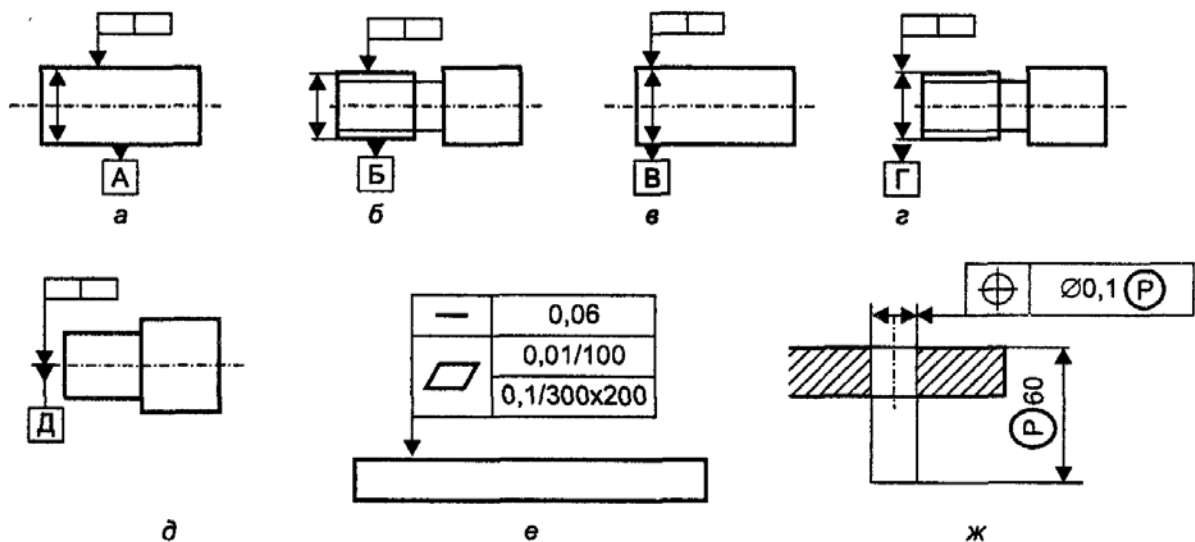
Правила простановки допусков формы и расположения
